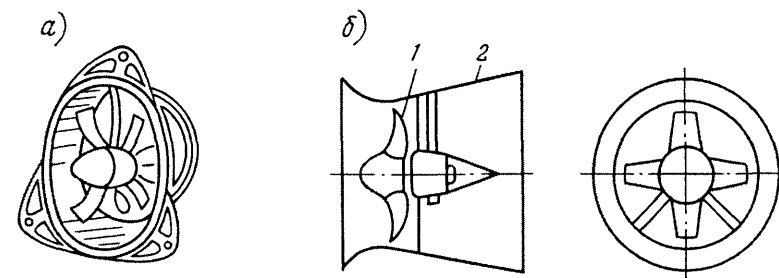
Общий вид (а) и схема устройства (б) осевого вентилятора 1 — осевое лопаточное колесо; 2 — цилиндрический корпус (кожух)
